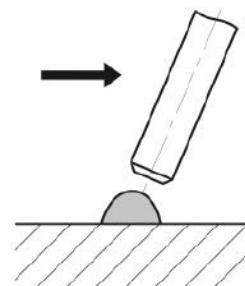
Влияние длины дуги и скорости сварки.
